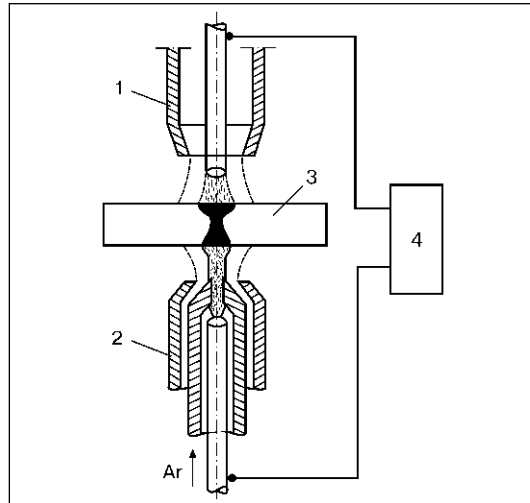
Схема процесса сварки встречными дугой и плазмой
